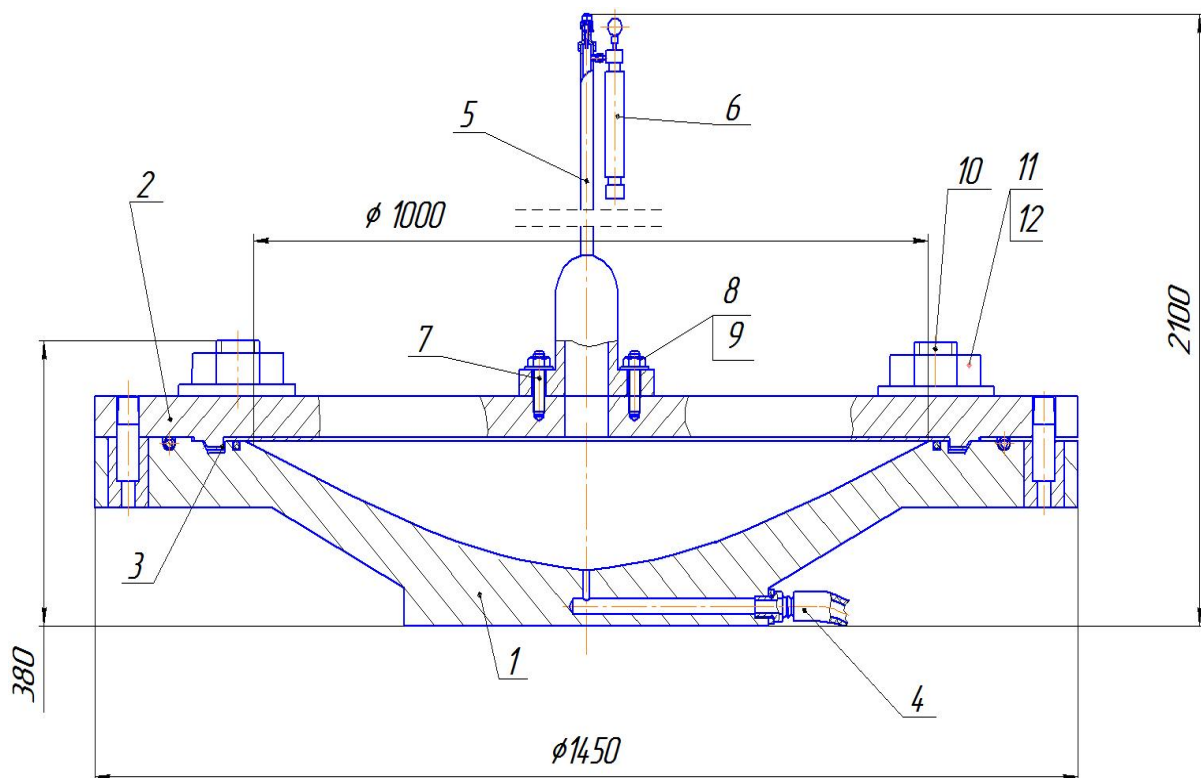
Устройство для импульсной штамповки крупногабаритных изделий: 1 – матрица; 2 – прижимная плита; 3 – заготовка; 4 – гибкий вакуум-шланг; 5 – пневмо-газодетонационное устройство; 6 – газогенератор; 7, 8, 9 – элементы крепления импульсной камеры к прижимной плите; 10, 11, 12 – шпилька, гайка, шайба для прижима заготовки к матрице
